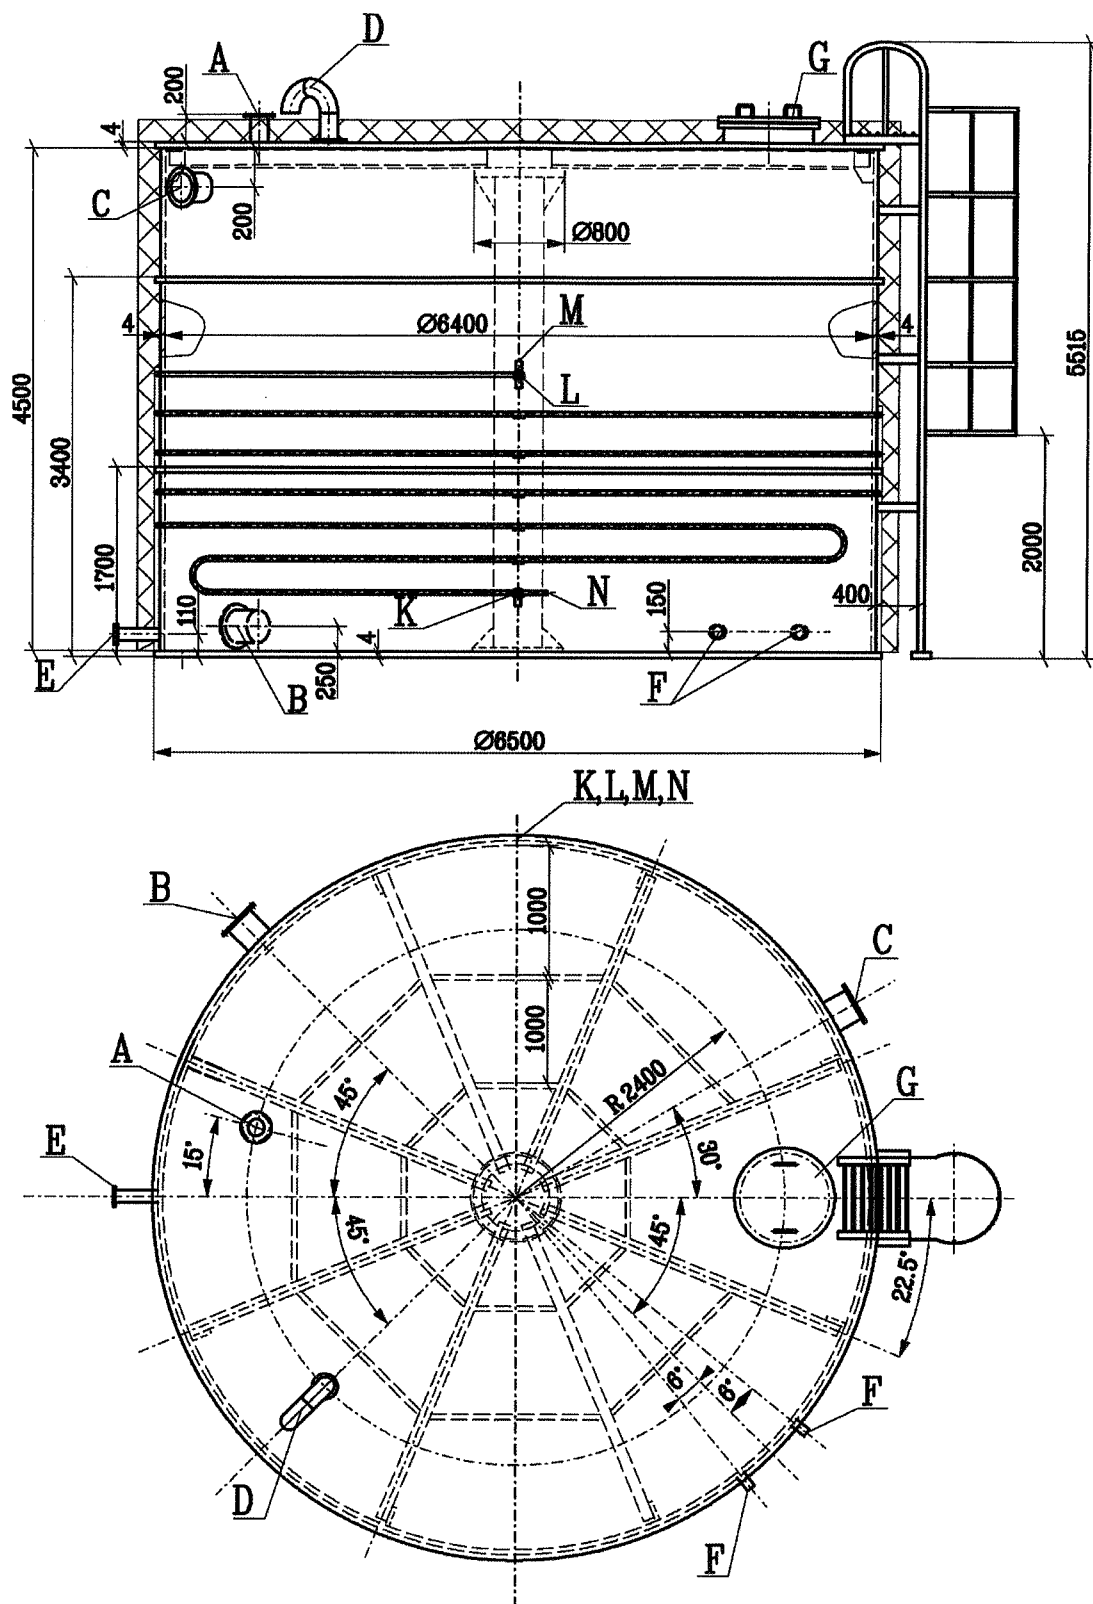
Габаритный чертеж бака обессоленной воды GDF90BB001, GDF90BB002
